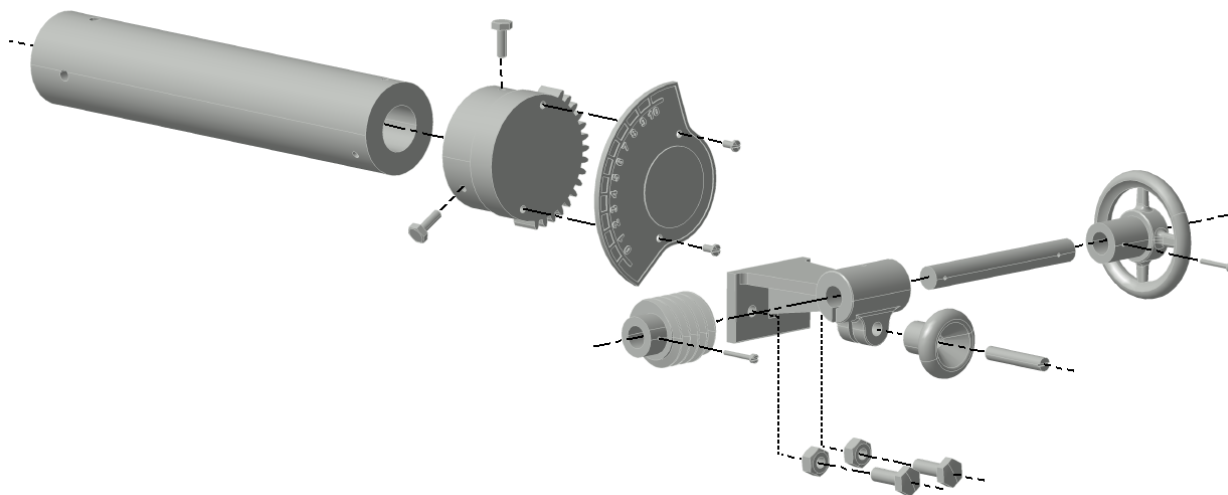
Vista explosionada del regulador de inclinación del canalón.
